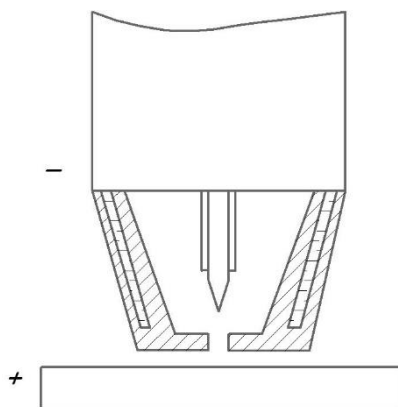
Схема плазменной сварки на прямой полярности
